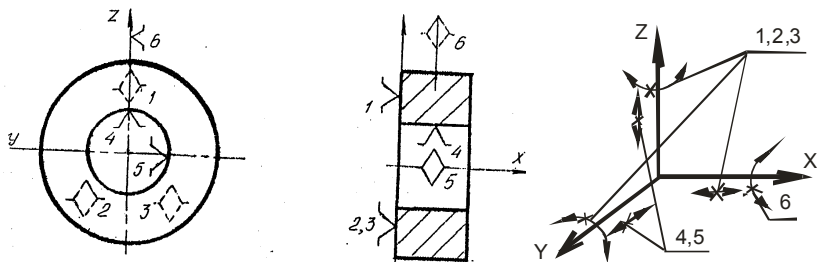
Теоретическая схема базирования заготовки по плоскости и внутренней цилиндрической поверхности (короткое цилиндрическое отверстие)
